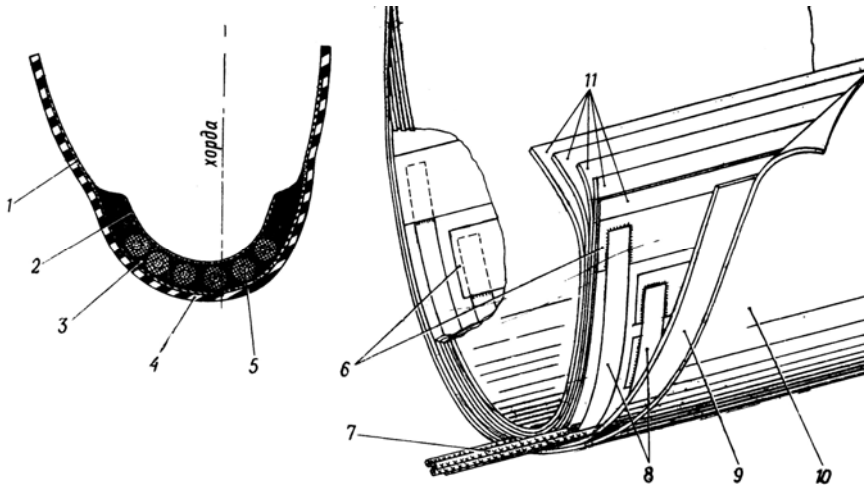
Нагревательная накладка лопасти несущего винта: 1, 2 – слои стеклоткани; 3 – резина; 4, 10 – поверхностный слой резины; 5, 7 – силовые провода; 6 – нагревательный элемент; 8 – соединительные шины; 9 – наружный слой стеклоткани; 11 – внутренний слой стеклоткани
